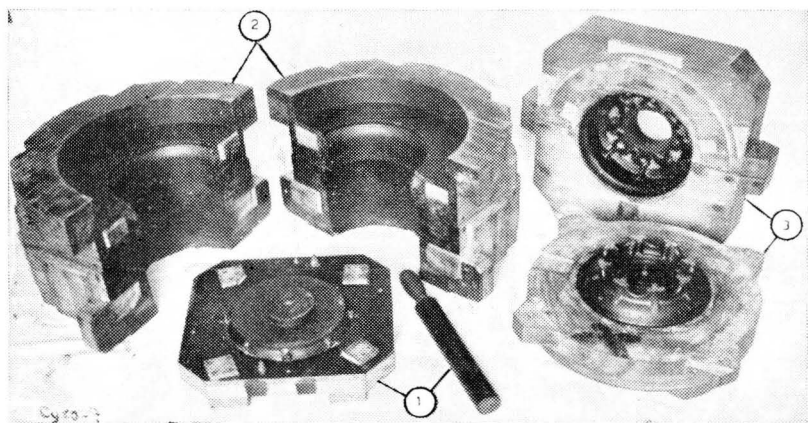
Caixas de macho para pistões de motor de locomotiva Diesel-elétrica. Os números 1, 2 e 3, indicam a base, o corpo e a cabeça dos machos, respectivamente.
